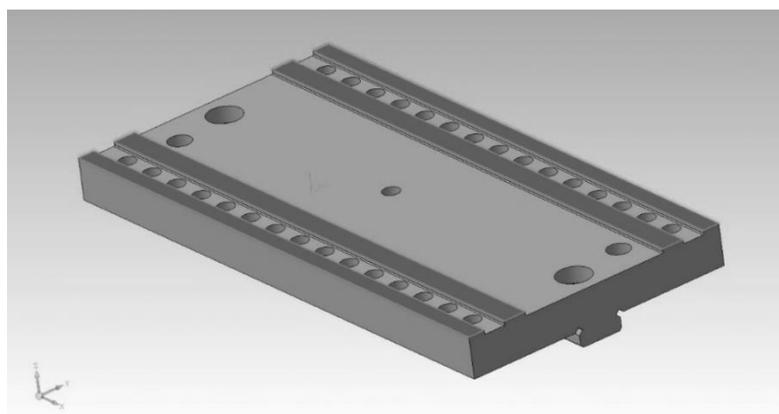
Основание гребёнки прибора для контроля лопаток
